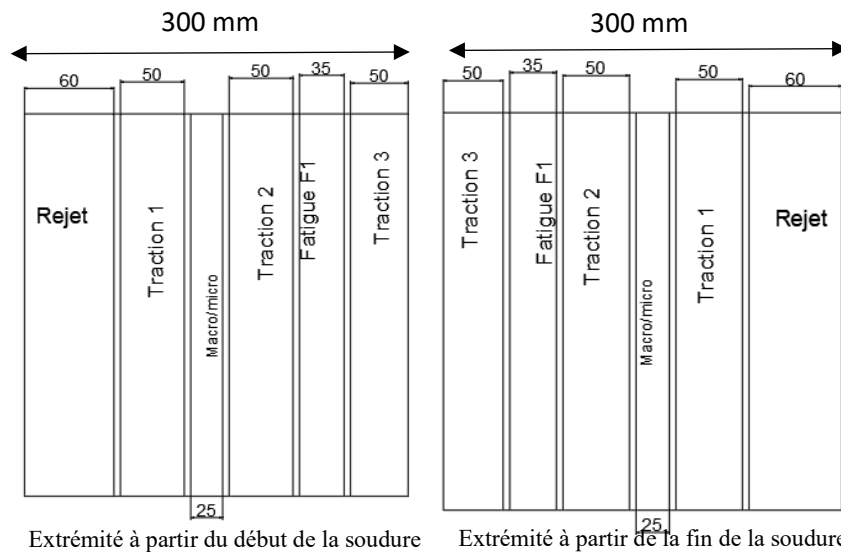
Plan d'usinage pour les tests finaux aux extrémités de l'extrusion (dimensions en mm)
